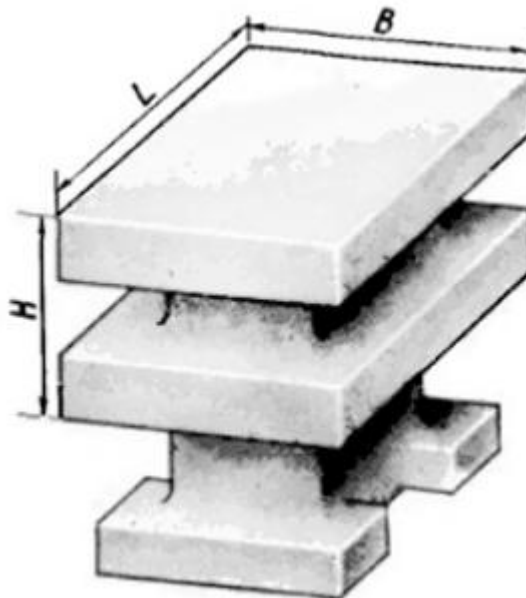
Форма образца для проверки точности вертикально-фрезерного станка
